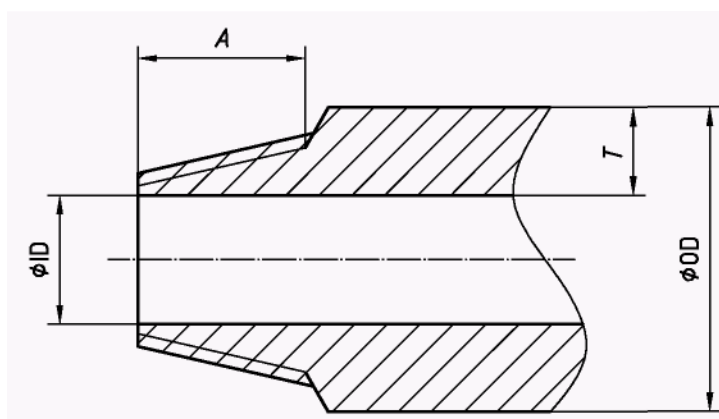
Патрубок с резьбовым торцом для Класса 800
